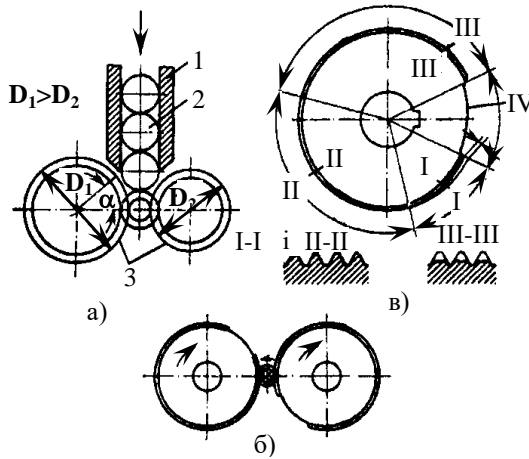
Накаткування різь роликми з тангенціальною подачею заготовок:
